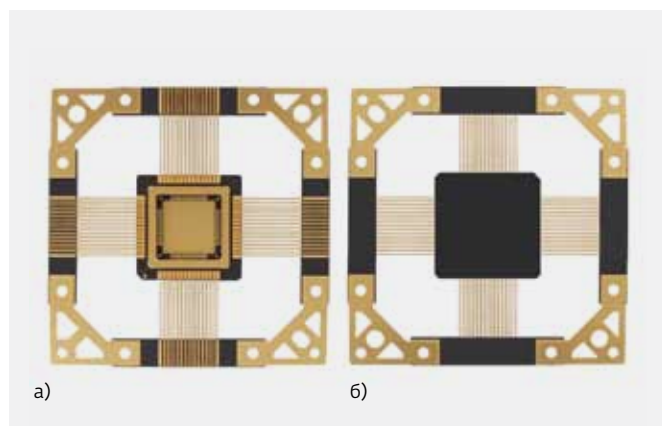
Корпус МК 4239.68-1 с верхним расположением выводов: а) вид сверху, б) вид снизу
